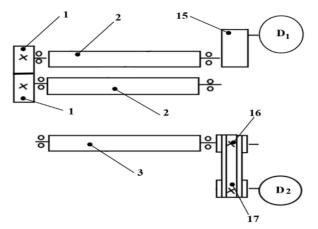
Кинематика роликов и стопочного барабана, обеспечивающая джин-машину новой конструкции.
